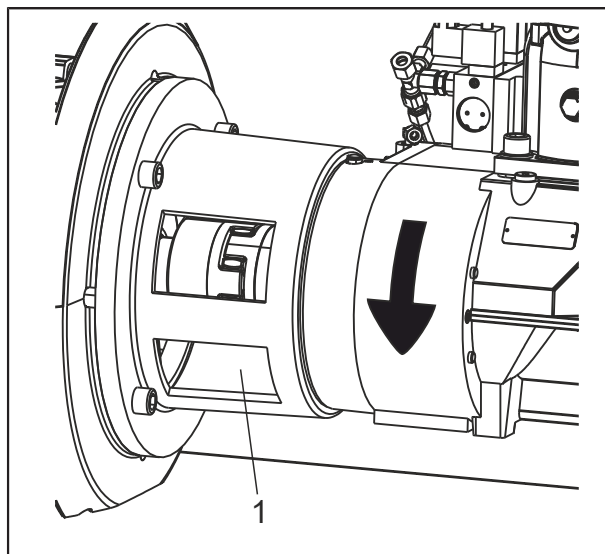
Kontrol af gearkompressorens drejeretning
